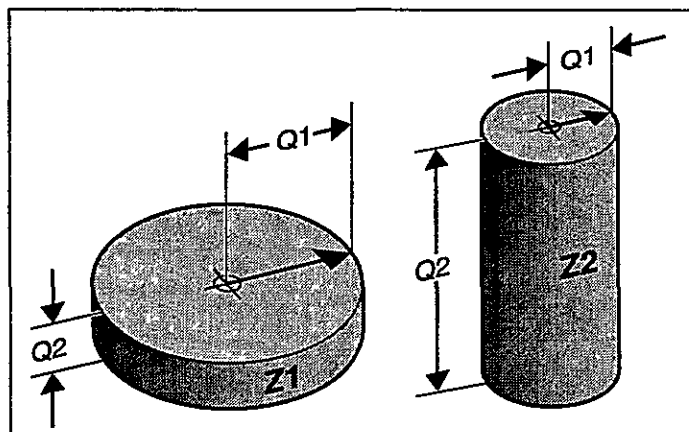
Dimensions d'une pièce sous forme de paramètres Q
